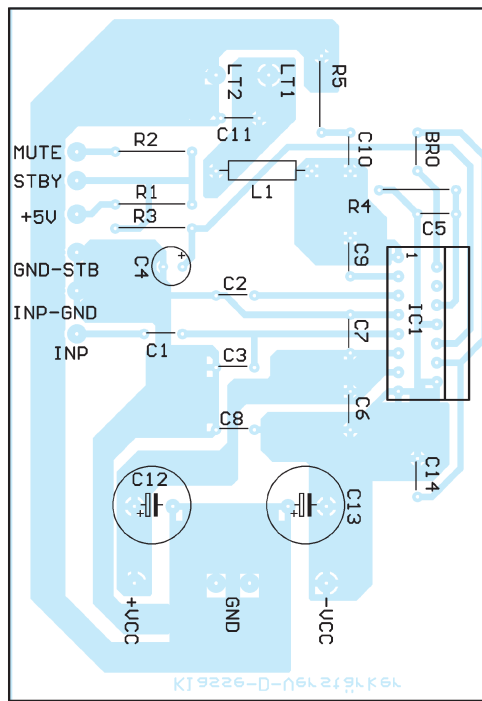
Die wenigen Bauelemente sind schnell bestückt.
